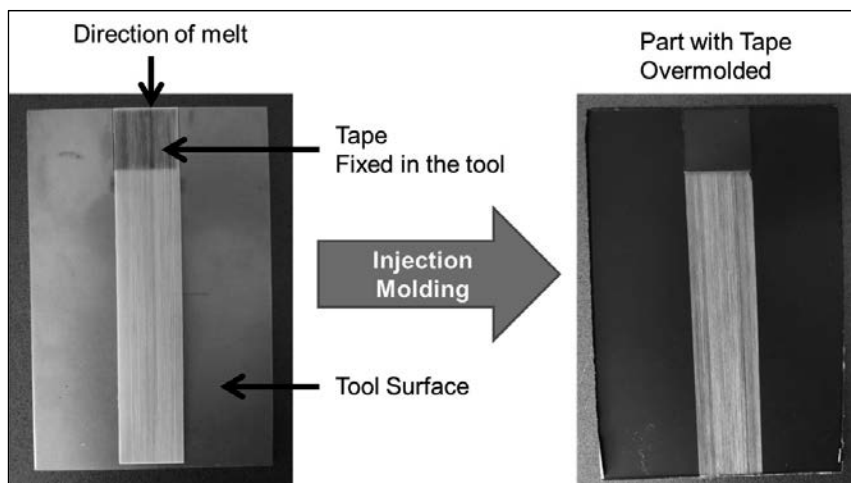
Celstran® Tape Fixierung im Spritzgusswerkzeug (Klebe- oder Magnetfixierung)
